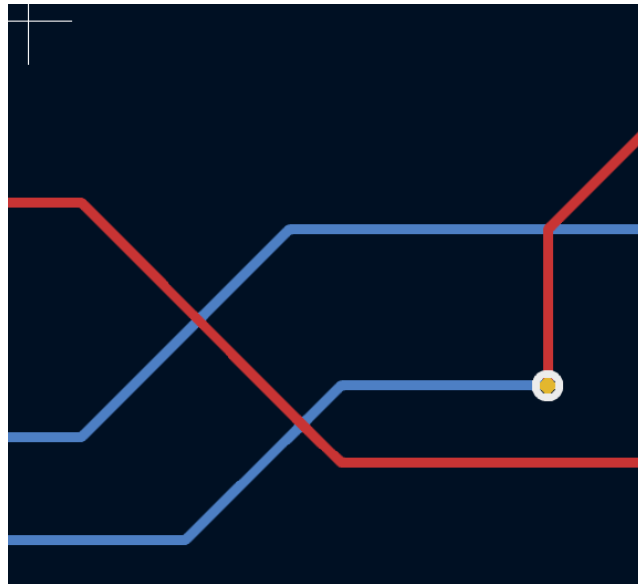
Via (en jaune) permettant la connection de pistes sur des couches différentes
